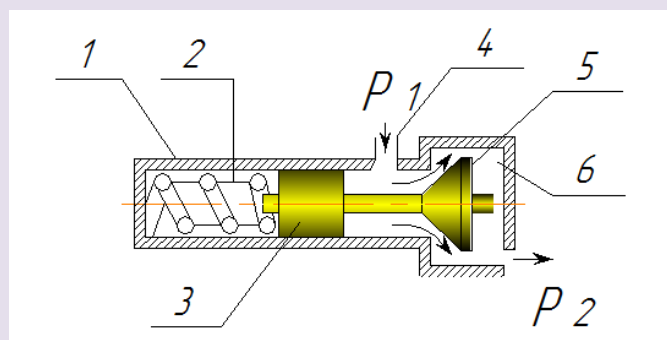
Клапан: 1– корпус клапана; 2– пружина; 3– поршень; 4– подводящий (напорный) канал; 5– конусный клапан; 6– камера
